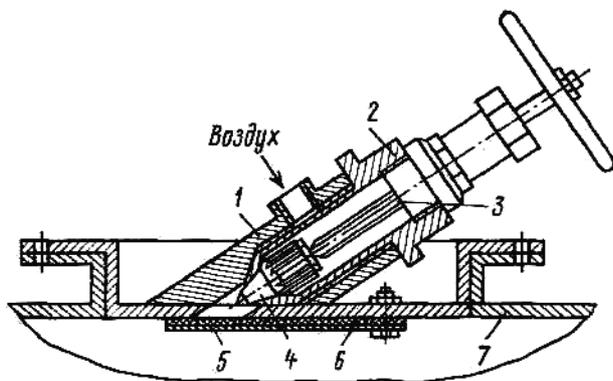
Пневмоэжектор: 1 — патрубок; 2 — корпус эжектора; 3 — шток; 4 — запорное устройство; 5 — стальная пластина; 6 — резина; 7 — трубопровод
